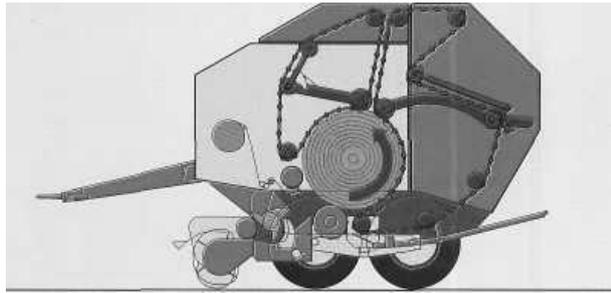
Схема пресс-подборщика с переменной пресс-камерой
